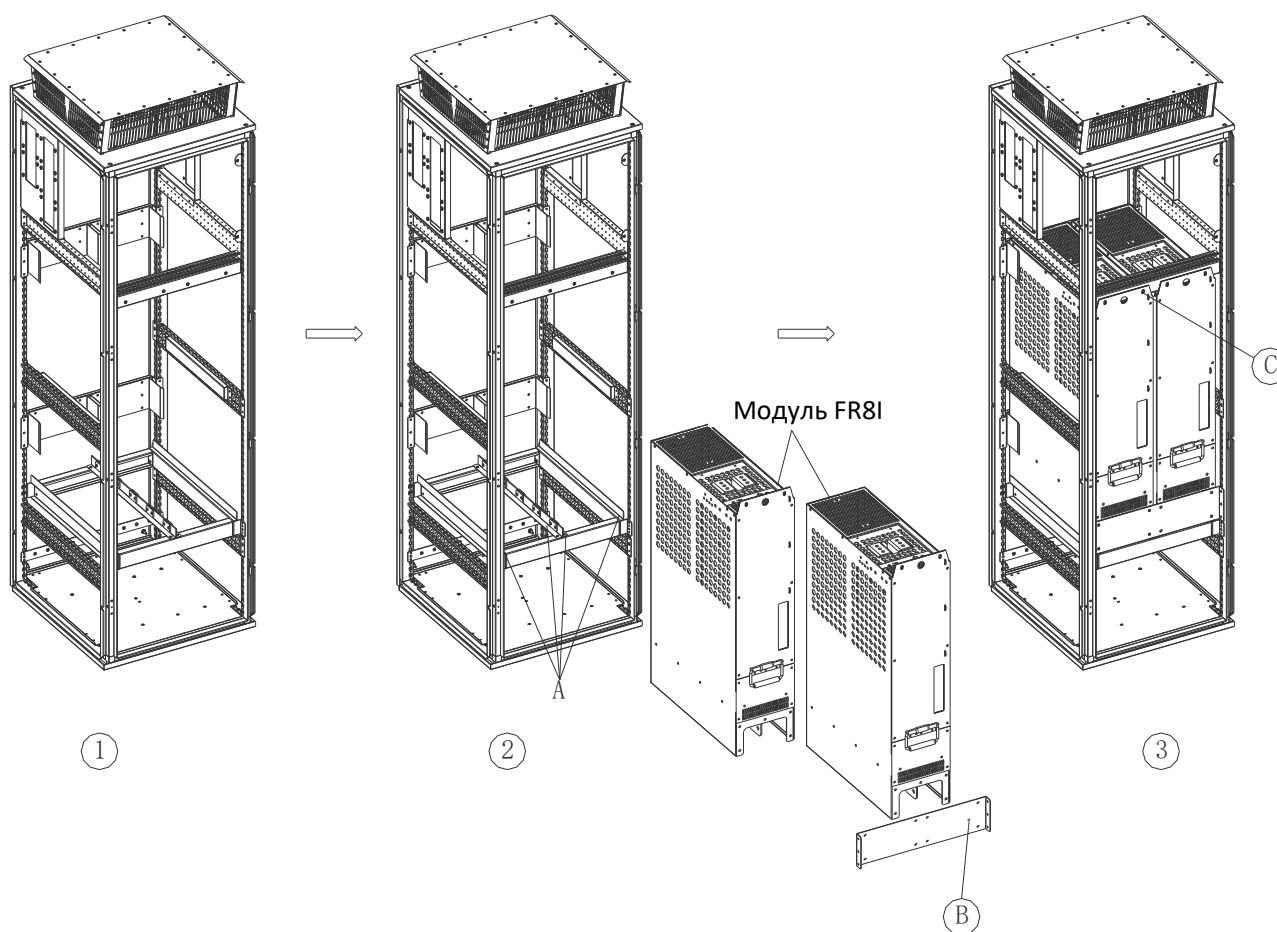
Схема последовательности действий по установке модуля корпуса FR8I
